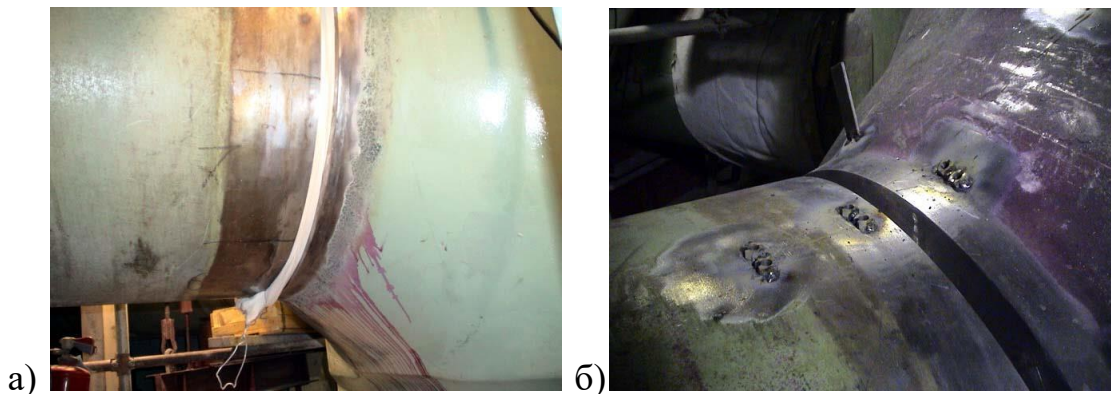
Собранный стык, подготовленный под сварку (а) удаление временных приспособлений (б)
